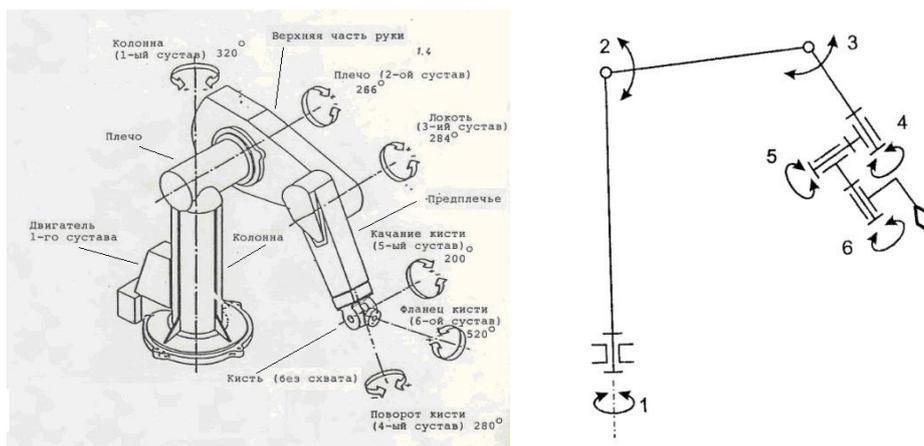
Общий вид и кинематическая схема манипулятора РМ-01
